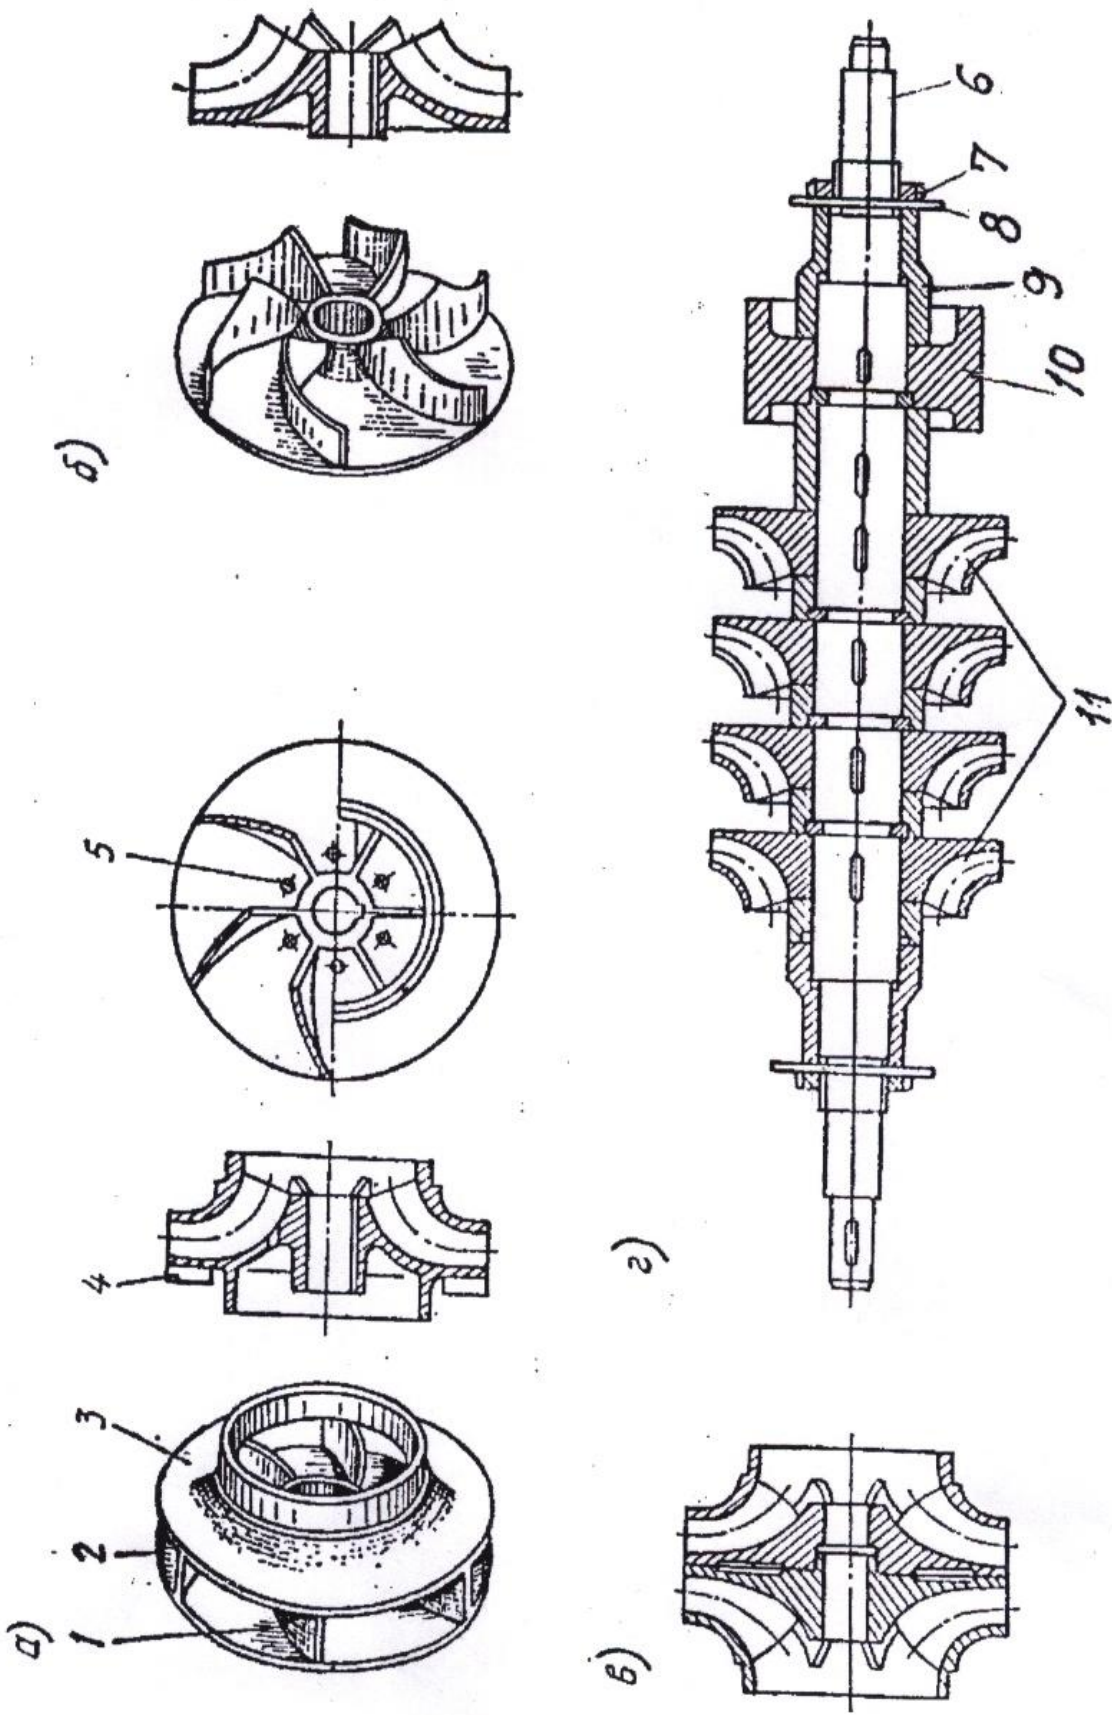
Рабочее колесо и ротор центробежного насоса:
